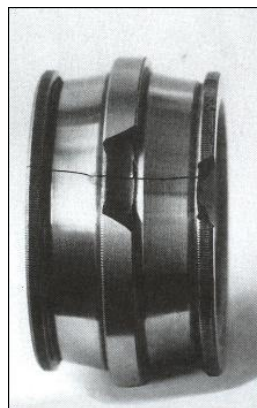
Fractura del aro interior de un rodamiento de rodillos a rótula. Uno de los rodillos ha sido extraído para permitir que el camino de rodadura en el lado izquierdo fuese examinado. El rodillo fue reinsertado con el martillo causando parte de la rotura de la pestaña central. Los impactos han sido transmitidos al camino opuesto a través de un rodillo, y parte de la pestaña también ha saltado. Al mismo tiempo el aro se ha fracturado transversalmente.
